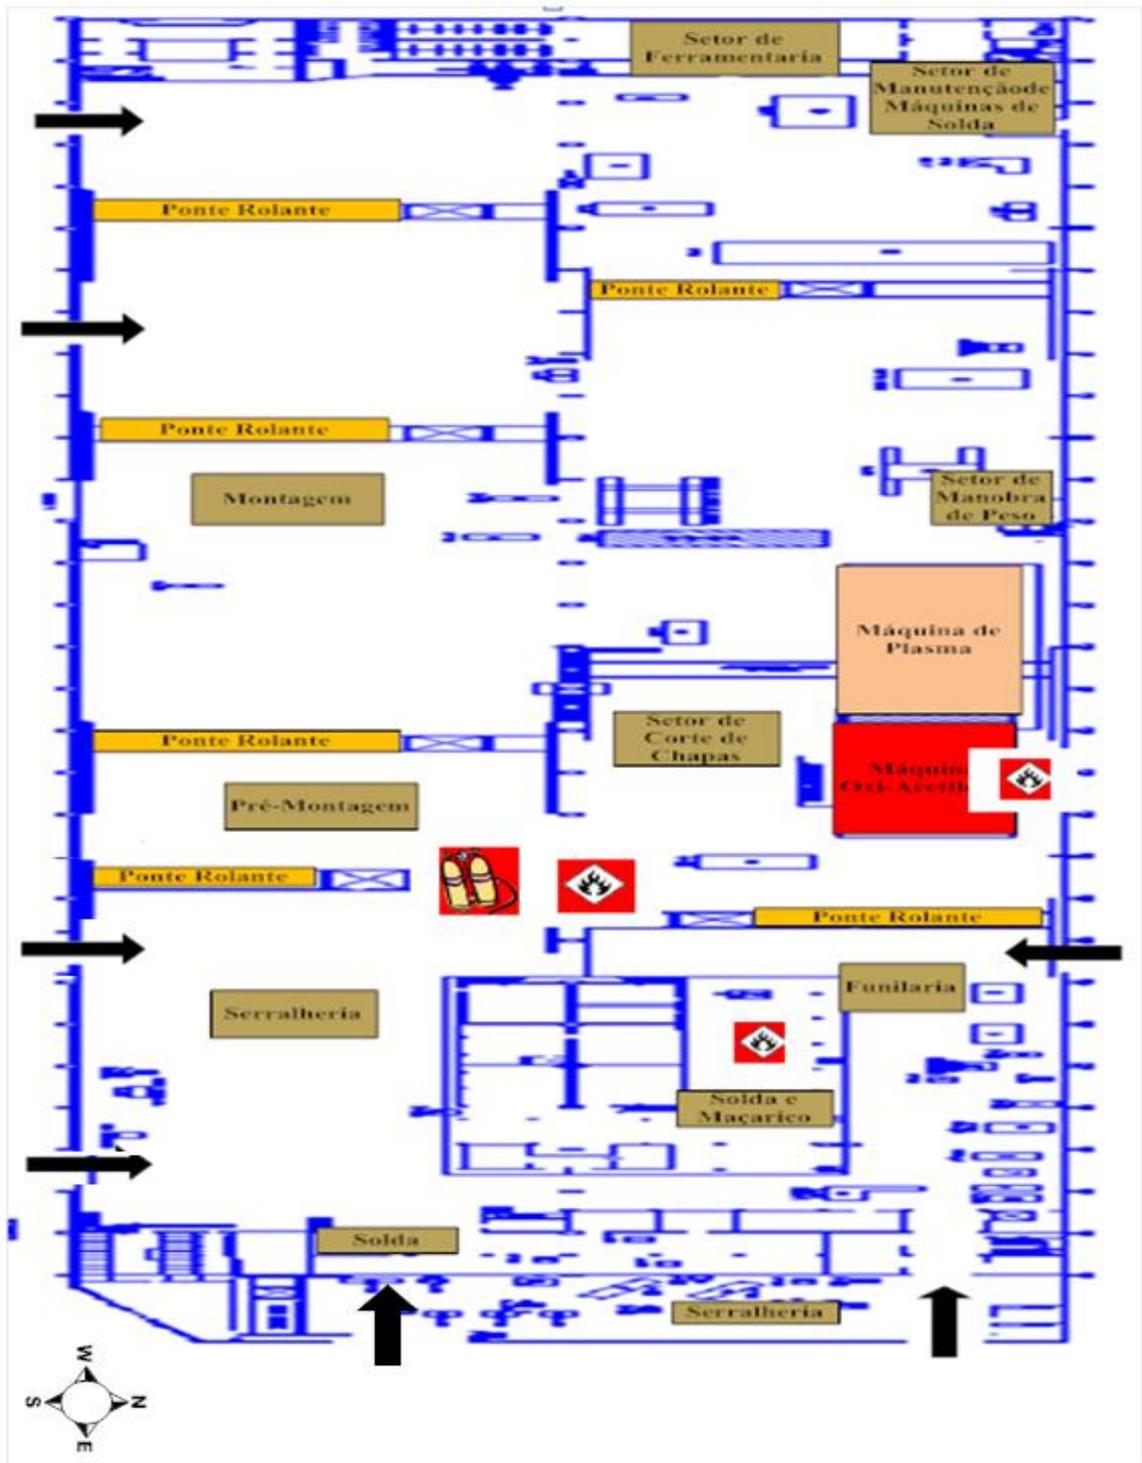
Planta Baixa da Divisão de Estruturas Navais. Fonte: documento interno da Organização e adaptação própria.
